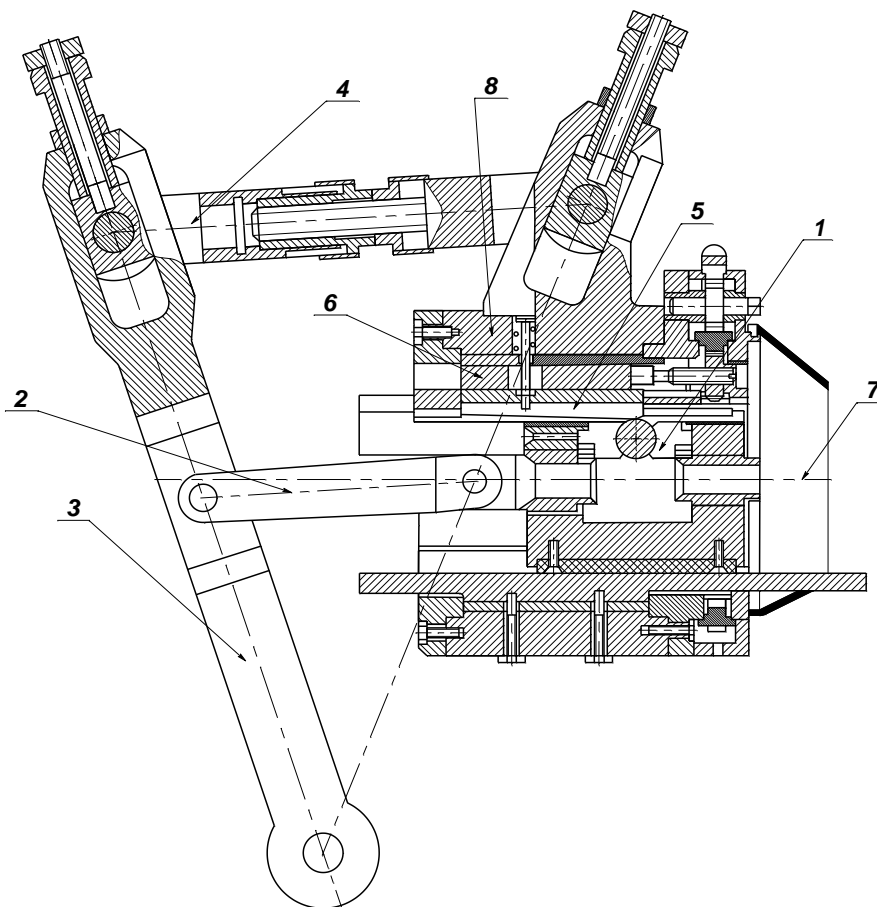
Клеть стана ХПТР в разрезе: 1 – сепаратор; 2 – тяга («серьга»); 3 – кулиса; 4 – тяга; 5 – калиброванная опорная планка; 6 – клин; 7 – линия прокатки; 8 – корпус
